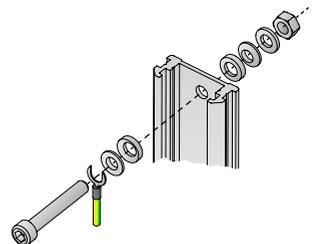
Befestigung mit Wandschrauben inkl. Erdkabel
